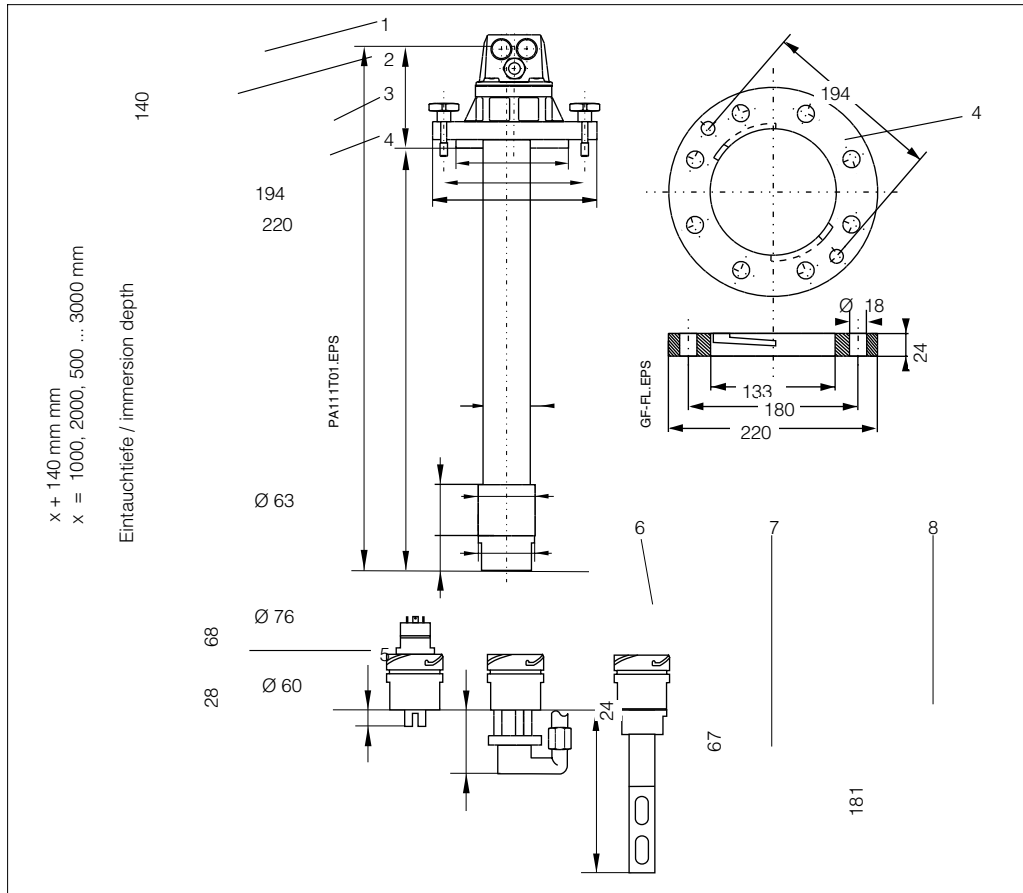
OLA 111 (links) Befestigungsversion A / C
